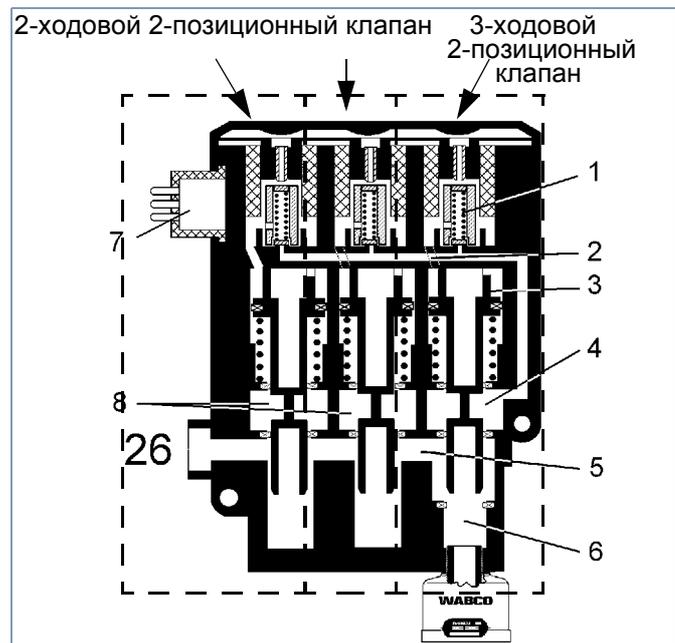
Изображение в разрезе магнитного клапана ECAS с золотниковыми клапанами пружинно-возвратного типа для главной оси или части главной оси (магнитный блок)
